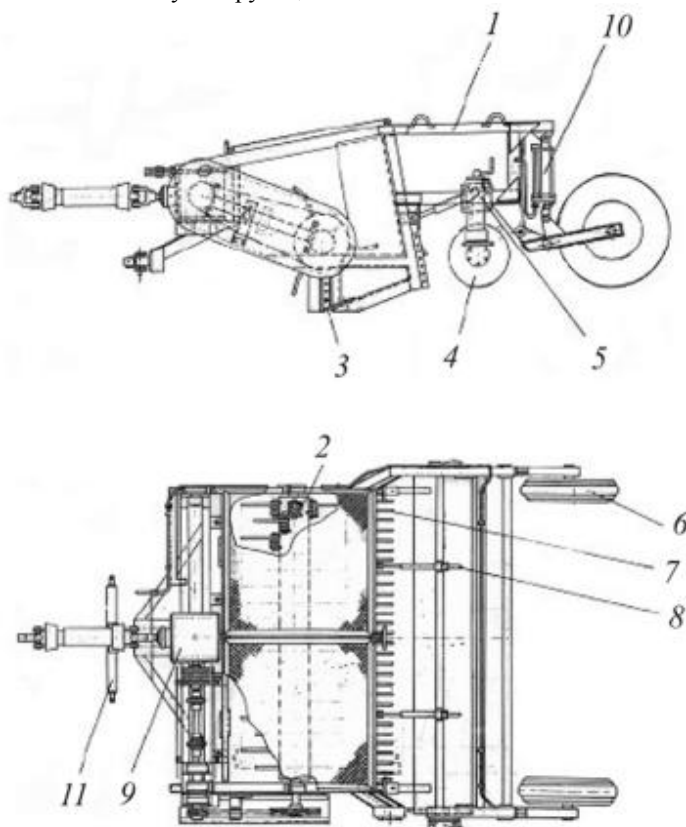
Машина роторная почвообрабатывающая МРП – 2,1: 1 – рама; 2 – ротор; 3 – лемех; 4 – каток; 5 – подвеска катка; 6 – колеса ходовые; 7 – дека; 8 – амортизаторы; 9 – механизм привода; 10 – гидросистема; 11 – прицепное устройство.
